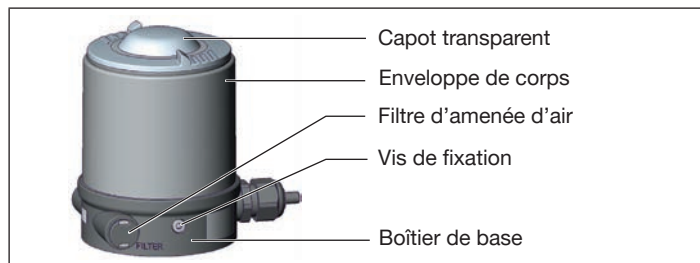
Construction, conduite d'air de pilotage intégrée
